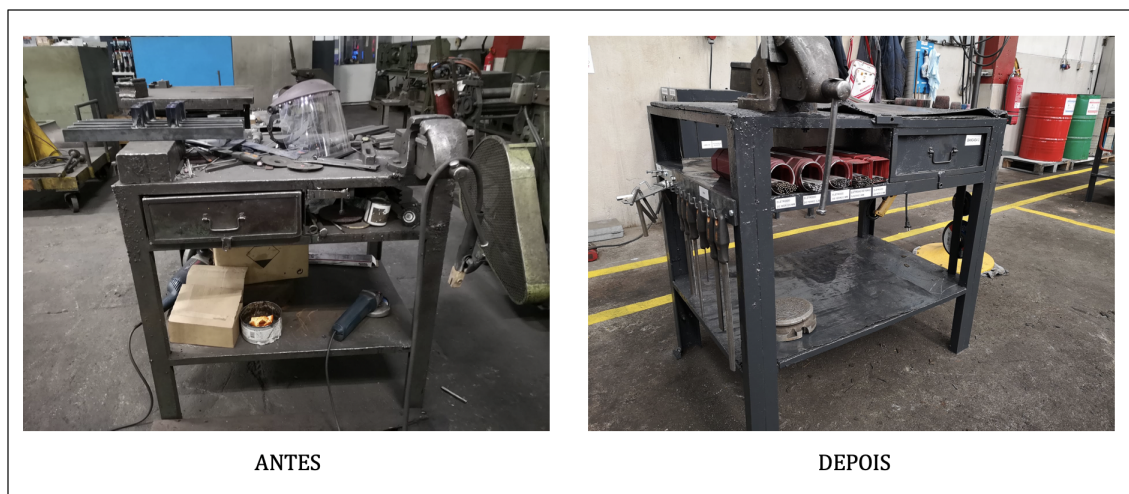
Ação 5s empresa ermesinde - vista detalhada.
